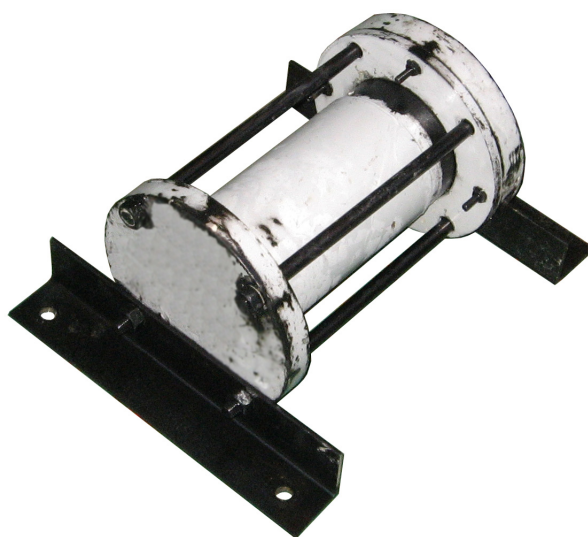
Общий вид гермобокса конструкции НГУ
